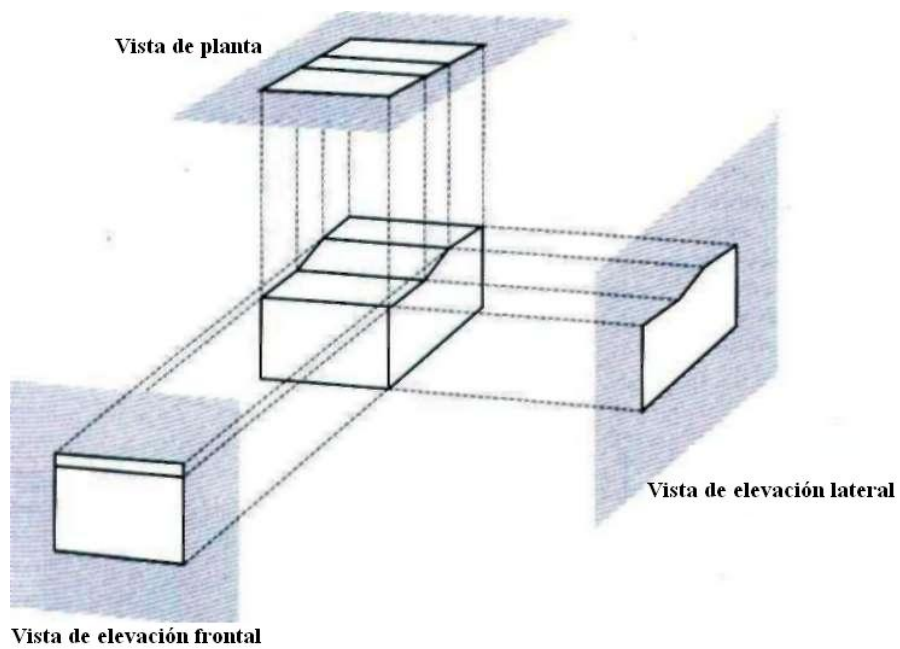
Proyecciones ortogonales de un objeto, donde se muestran la vista plana y las vistas de elevación.
